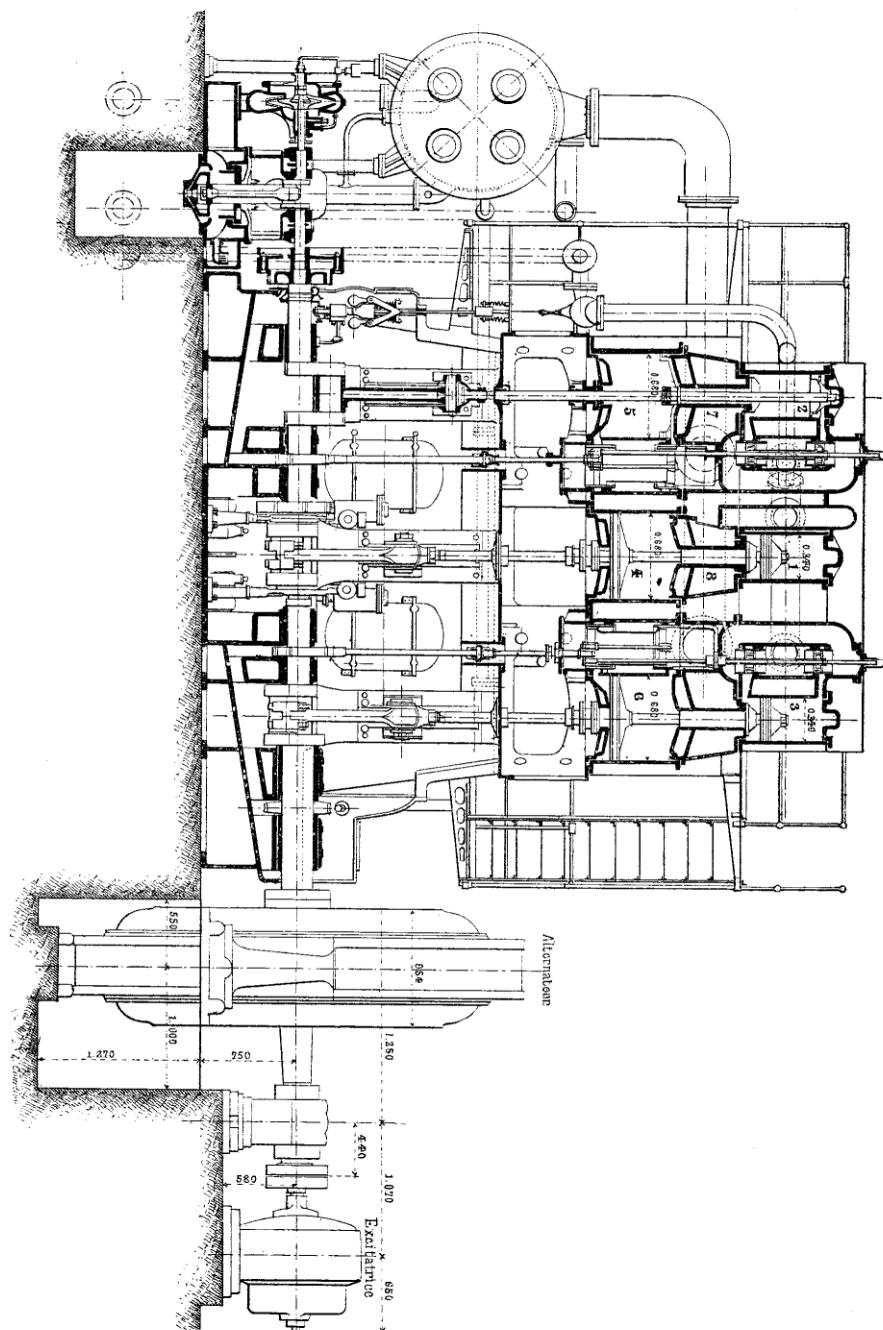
DELAUNAY-BELLEVILLE. — Coupe longitudinale.
